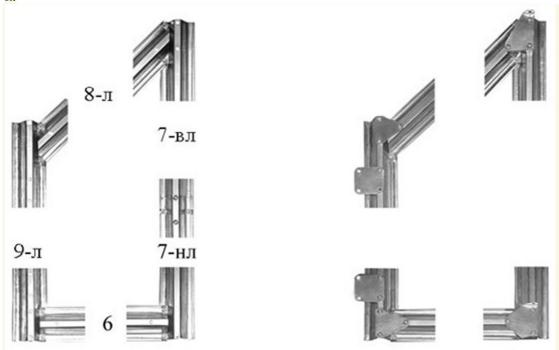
Сборка дверей. На рисунке показана сборка левой двери и установка на ней дверных накладок. Окончательную затяжку винтов делать после сборки всей двери и в процессе затяжки контролировать прямые углы нижней части двери.
